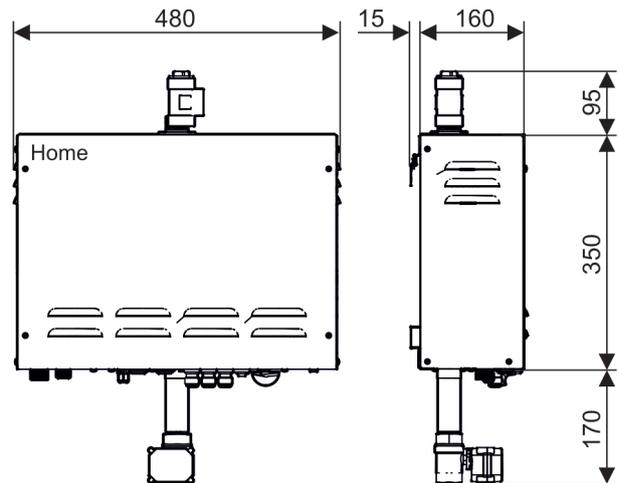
Générateur de vapeur de type Tylö Home, dimensions en millimètres
